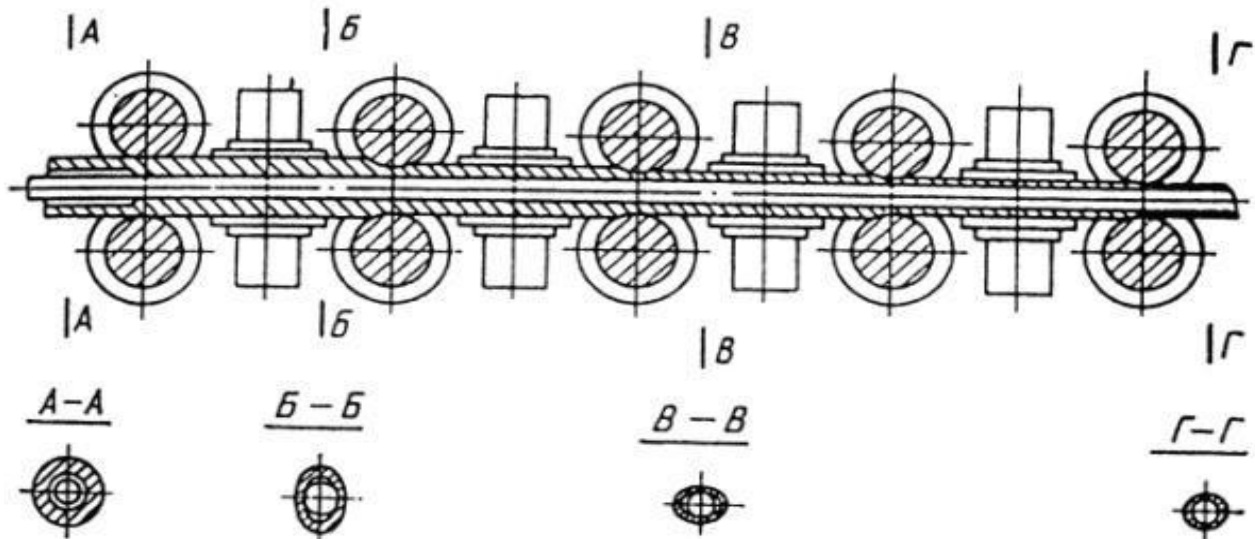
Розташування прокатних клітей безперервного трубoproкатного стану
